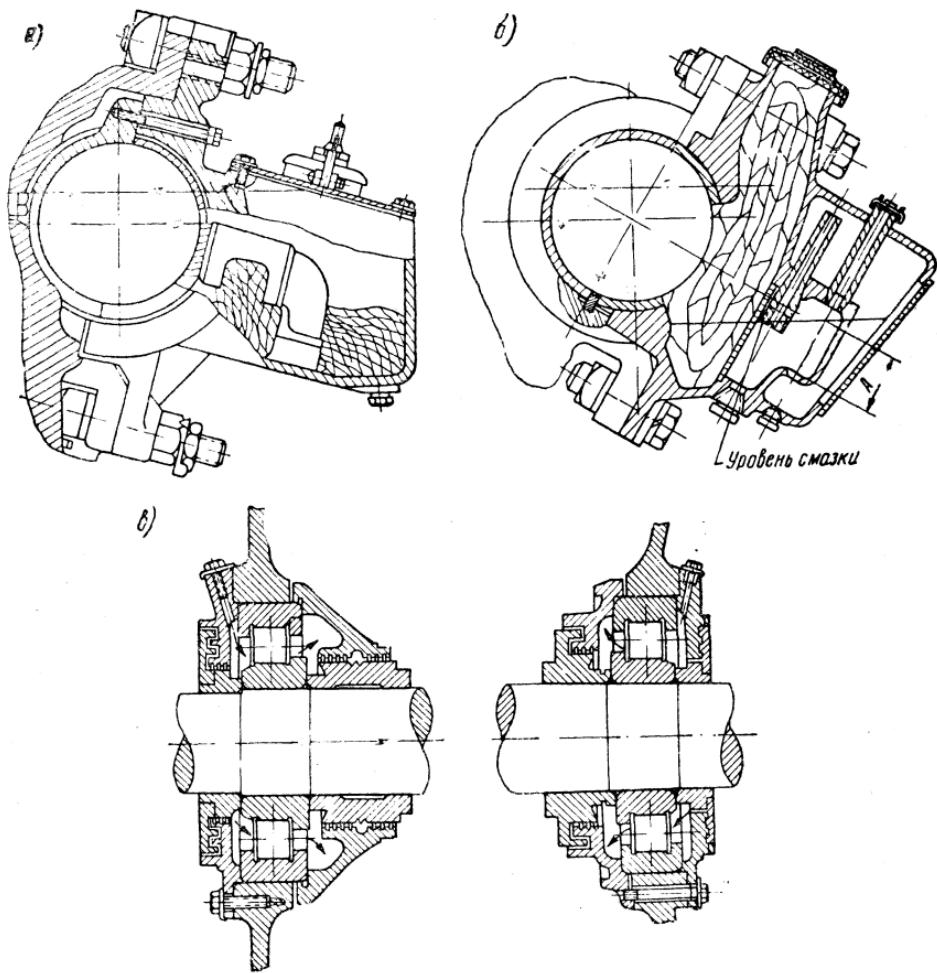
Система смазки подшипников тягового двигателя НБ-406Б:
